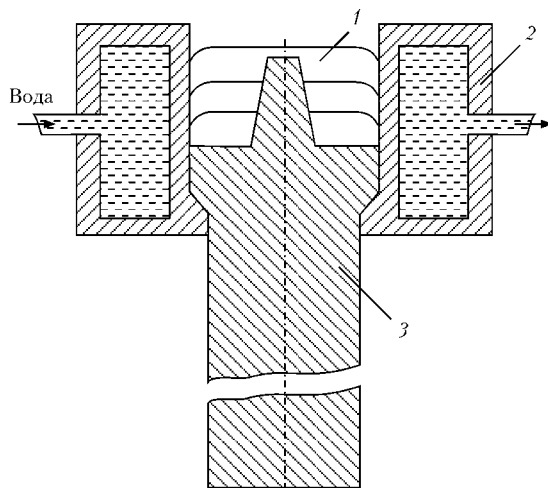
Схема ручной электродуговой наплавки штоков вентилей DN 50: 1 — наплавленный металл; 2 — водоохлаждаемый медный кокиль; 3 — заготовка штока
